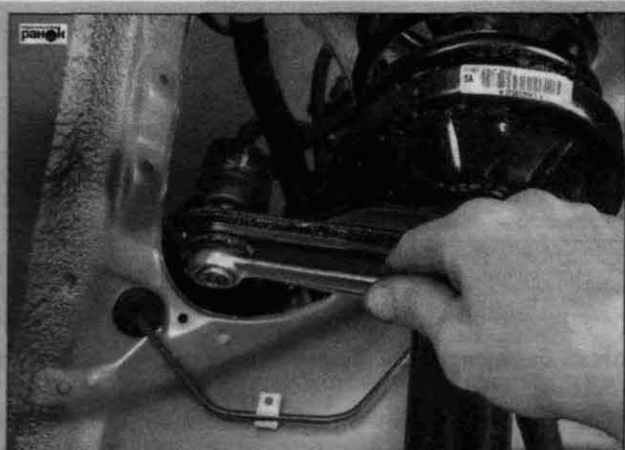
Отсоединение гайки крепления пальца шарового шарнира наконечника рулевой тяги
